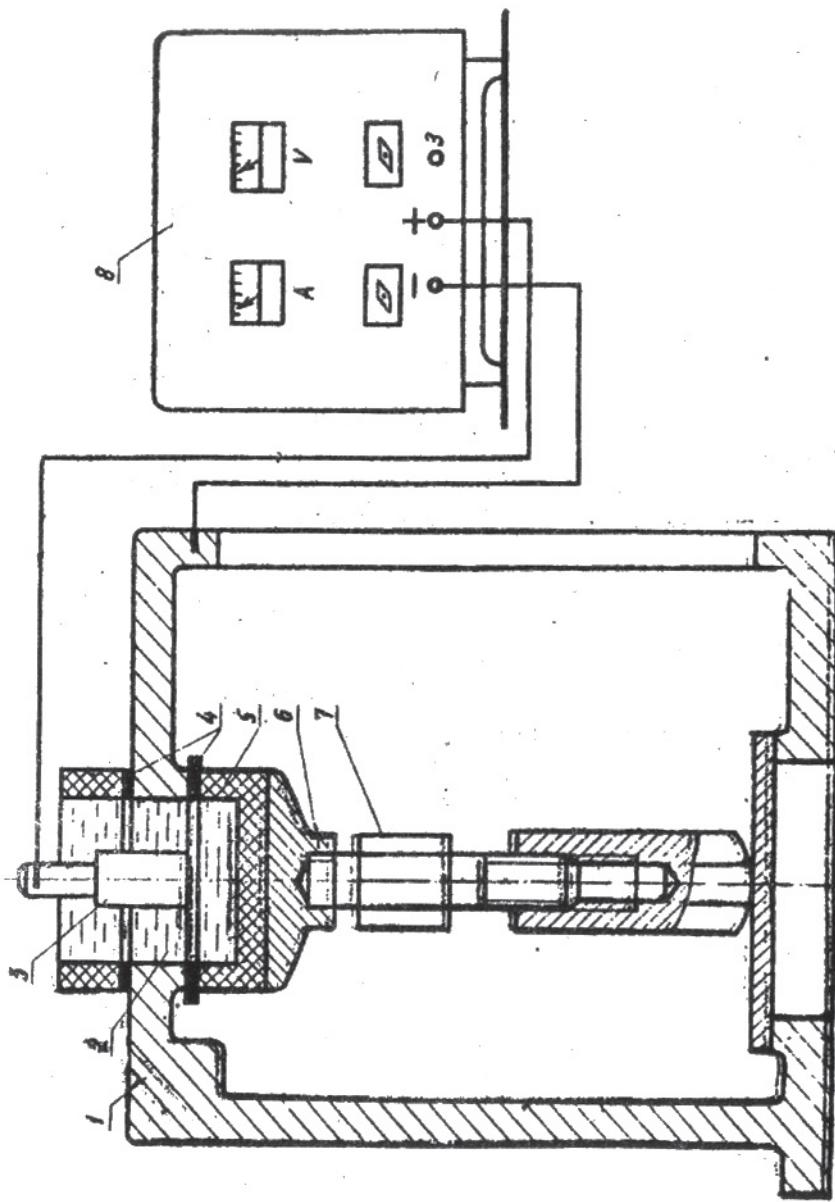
Схема внешнего железнения гнезд подшипников картера коробки передач: 1 - картер; 2 - электролит; 3 - анод, 4 - уплотнительная резина; 5 - стакан; 6 - стакан; 7 - крышка; 8 - распорка
